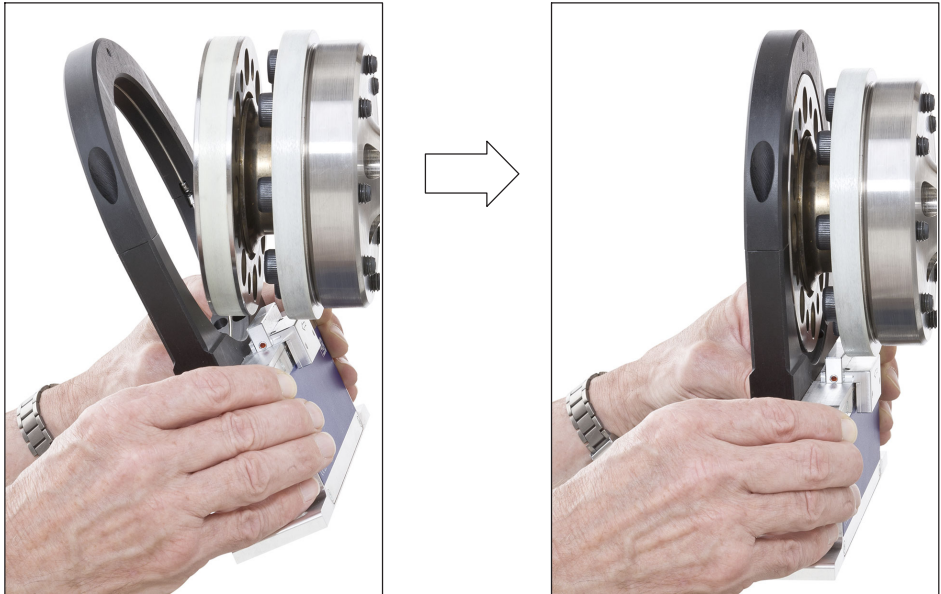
Ausrichten des Rotors mit dem Stator (mit Referenzimpuls-Sensor)
